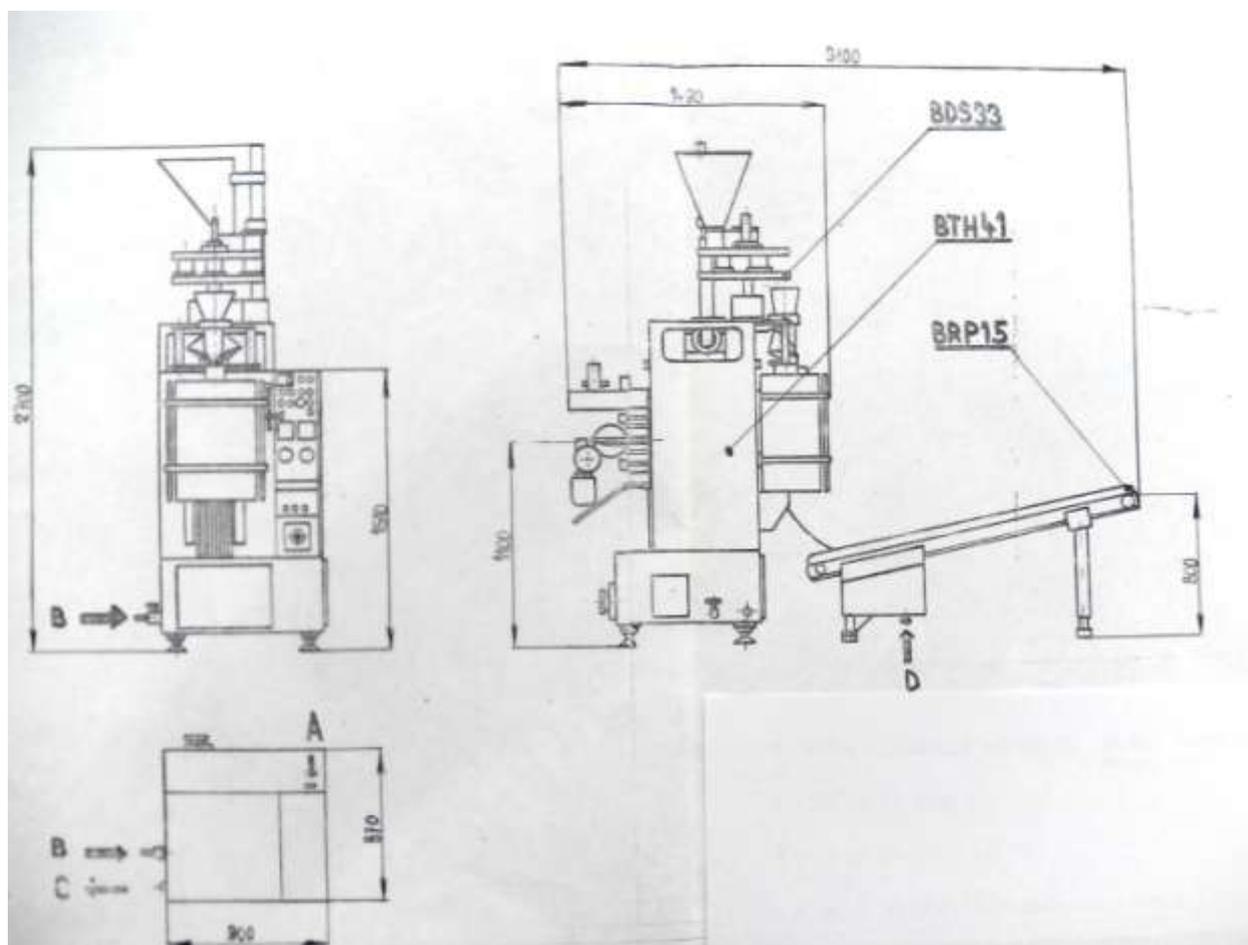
Фасовочно-упаковочный автомат ВТН-41.
